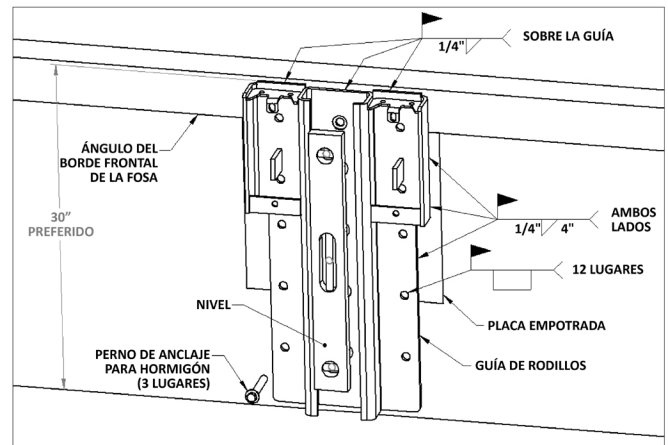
FIGURA D—VISTA FRONTAL DE SOLDADURA DE LA GUÍA DE RODILLOS (CON PLACA EMPOTRADA)
